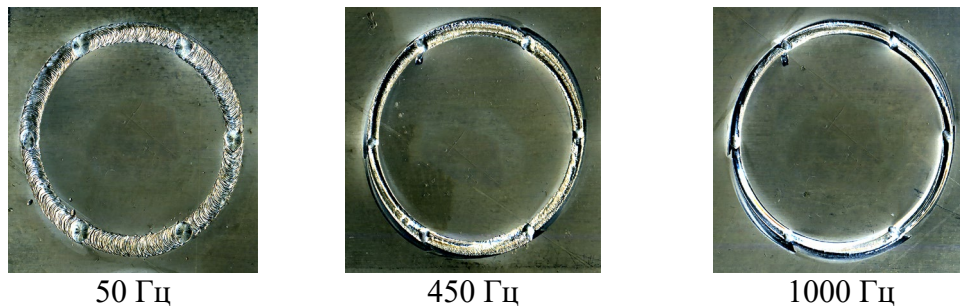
Внешний вид круговых сварных швов при 6-лучевой сварке
